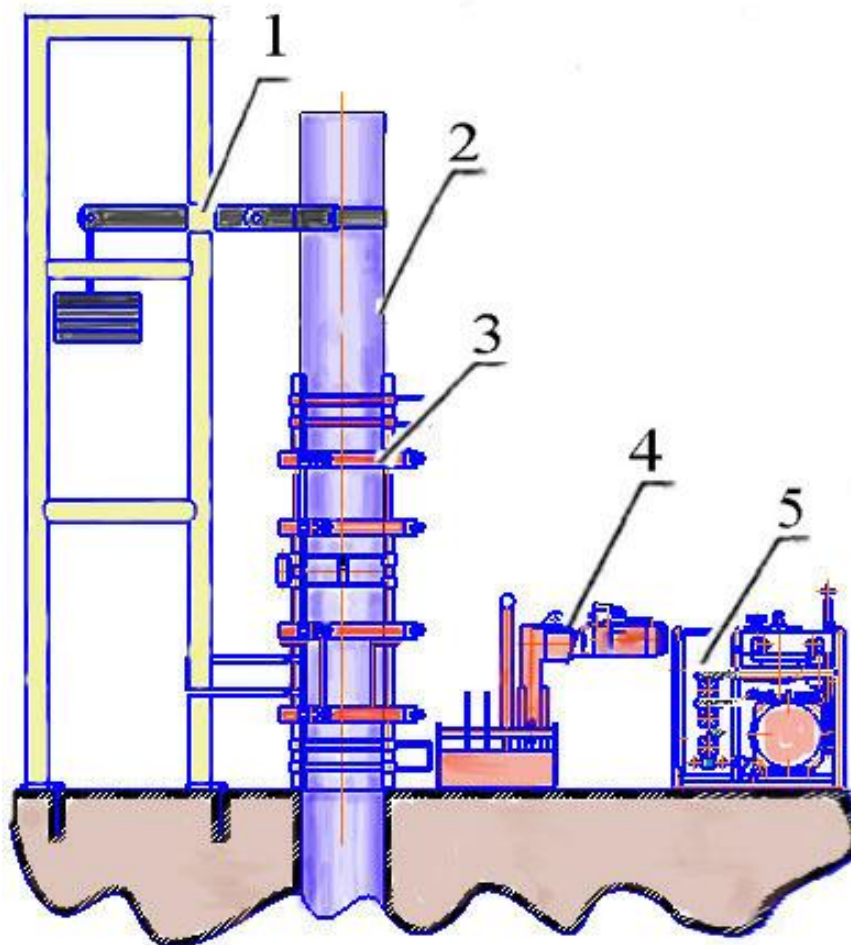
Схема участка для сварки полиэтиленовой трубы при строительстве скважины
